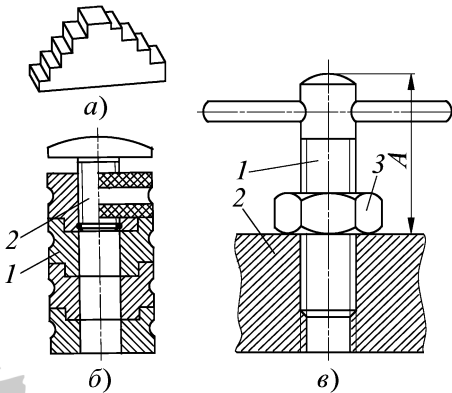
Конструкции штырей для установки заготовок:
